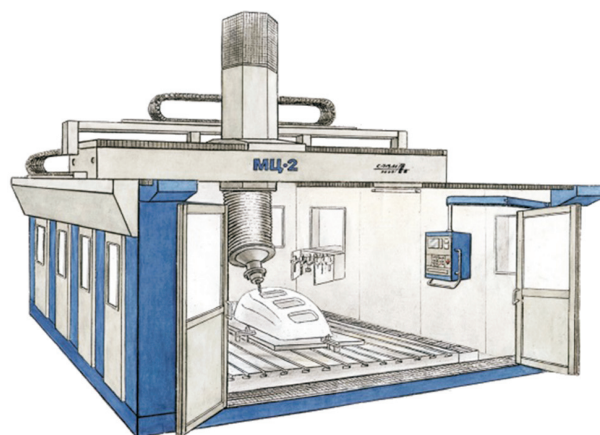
Внешний вид высокоскоростного пятикоординатного обрабатывающего центра МЦ-2
